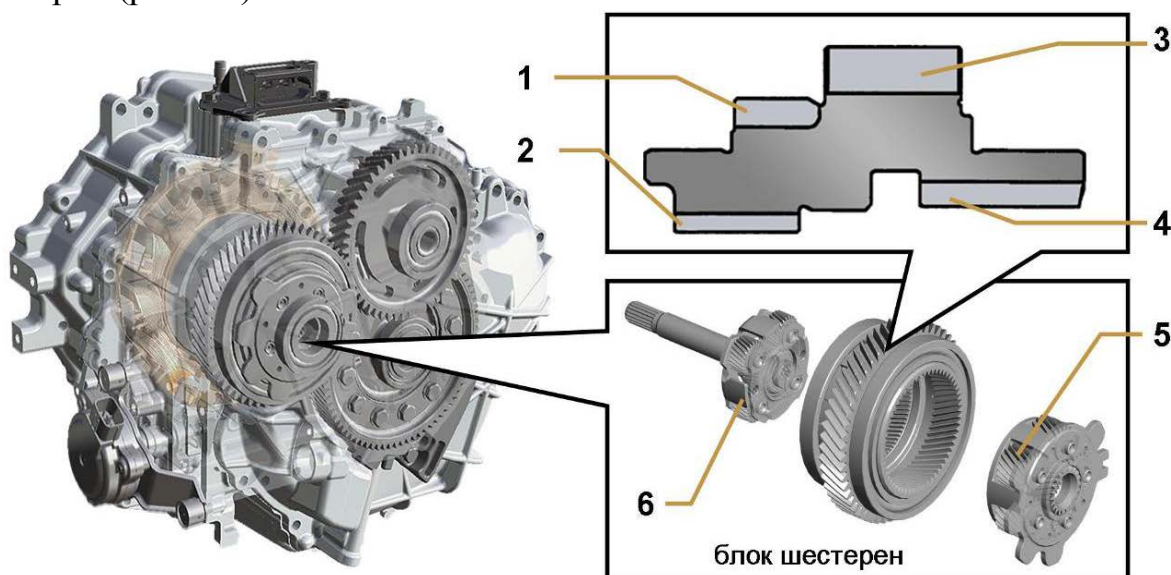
Блок шестерен трансмиссии P410: 1 - зубчатое колесо блокировки рычага селектора в положении «Р»; 2 - эпициклическое (коронное) зубчатое колесо планетарного редуктора MG2; 3 - ведущее промежуточное зубчатое колесо; 4 - эпициклическое (коронное) зубчатое колесо планетарного делителя мощности; 5 - планетарный редуктор MG2; 6 - планетарный делитель мощности
